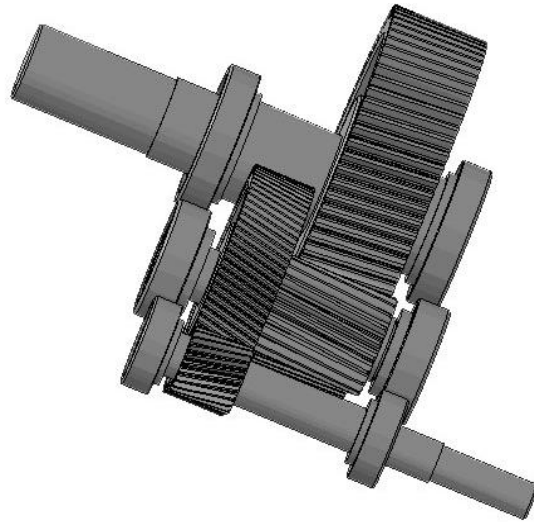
Зубчасті передачі редуктора в складеному вигляді
